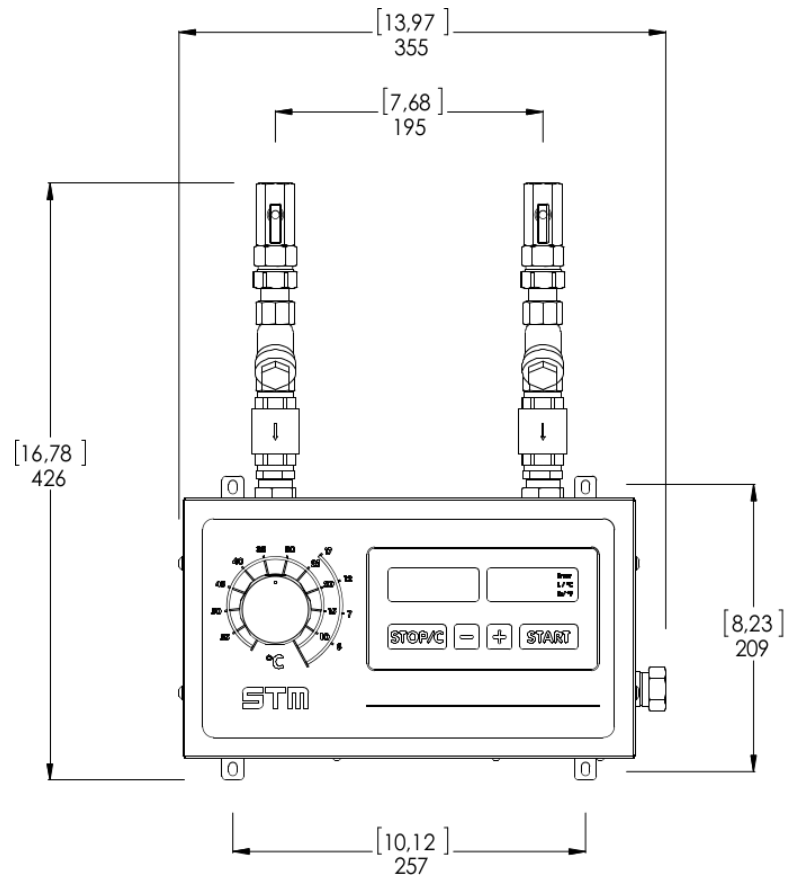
(Dimensioni; Dimensions; Dimensions)
